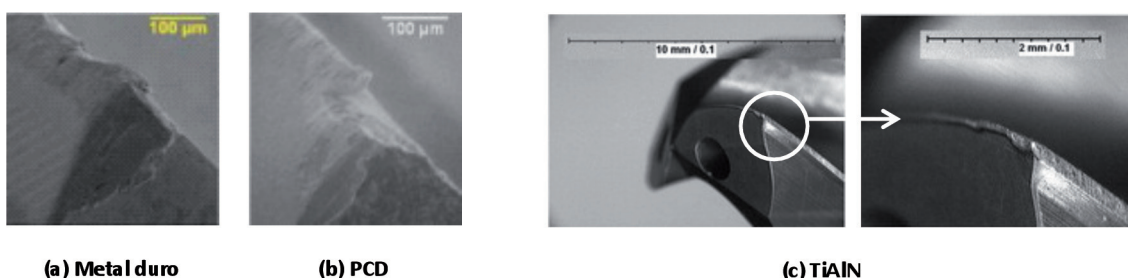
Desgaste de herramientas en el taladrado de stacks CFRP/Ti [10,11]
